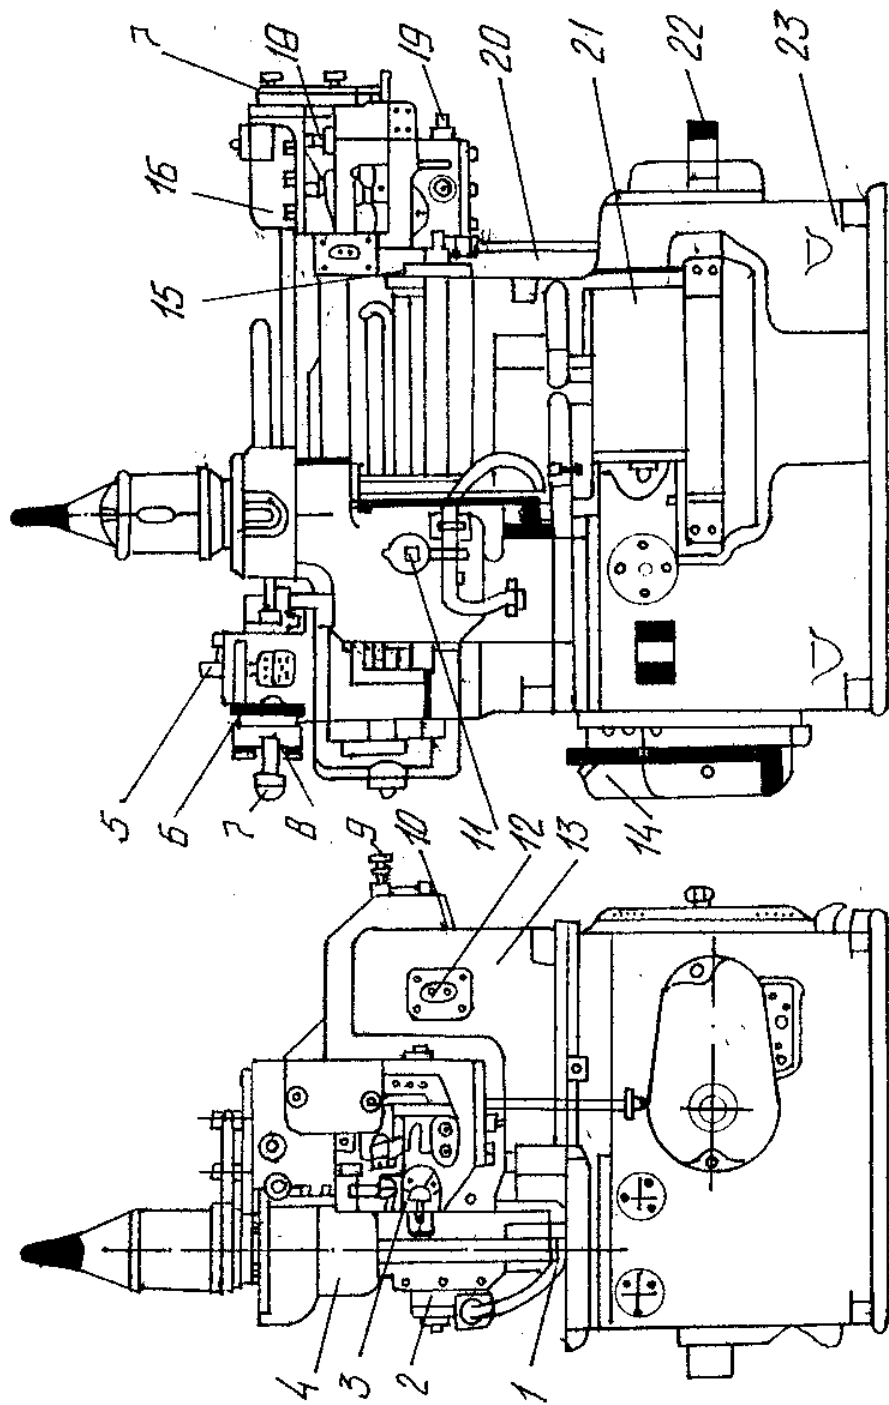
Общий вид зубодолбежного станка мод. 514
